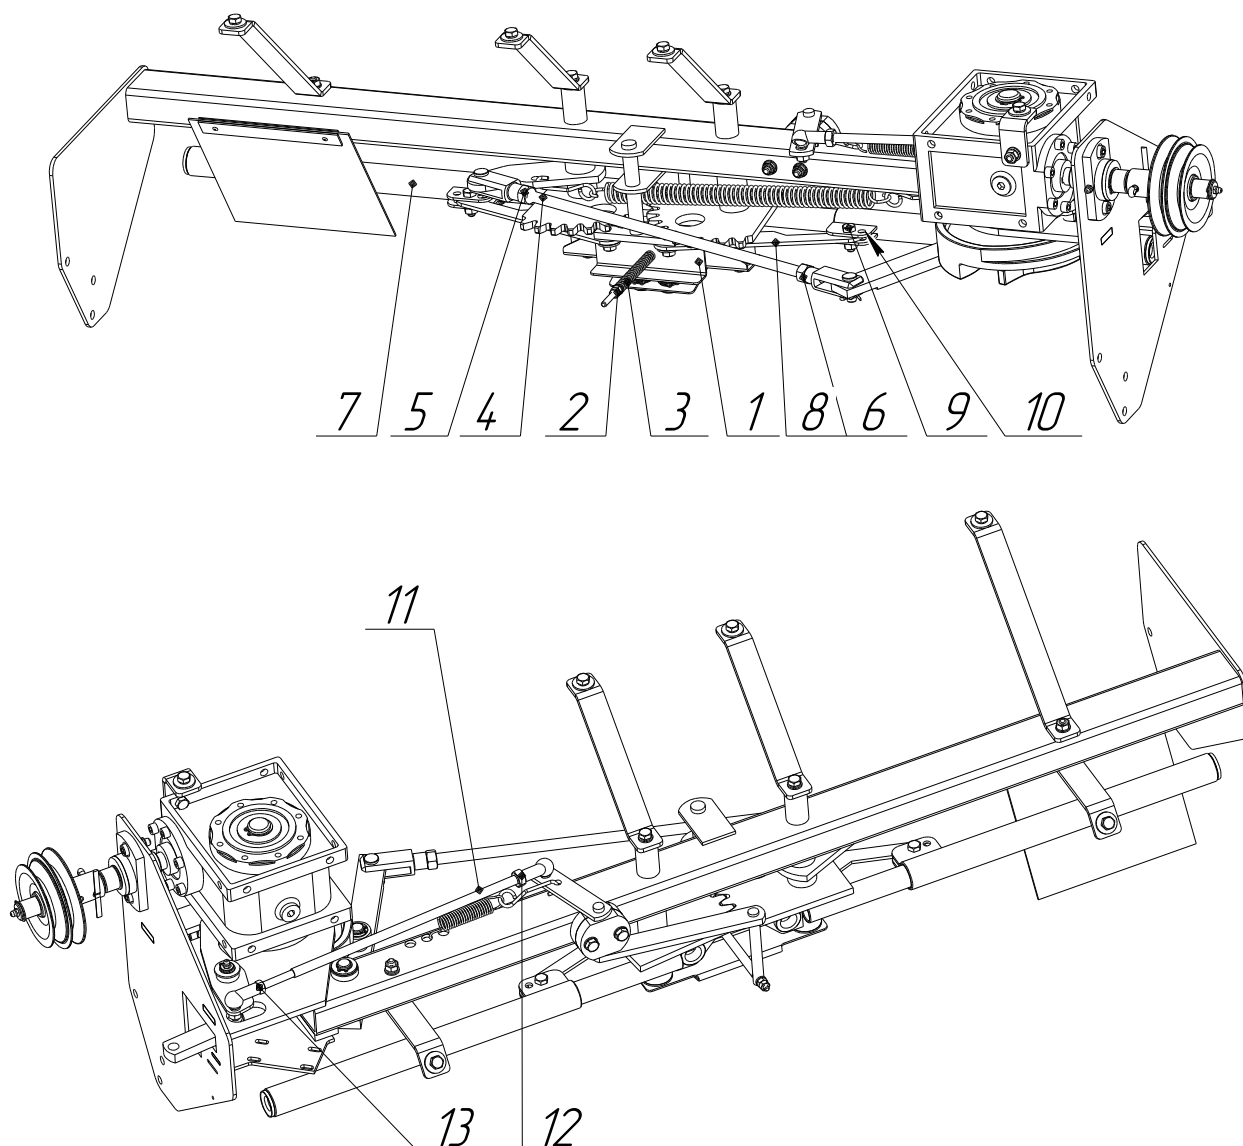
Регулировки механизма обвязки шпагатом: 1 – тормоз шпата; 2 – гайки М6; 3 – пружина тормоза шпата; 4 – тяга направляющих шпата; 5 и 6 – контргайки М12; 7 – направляющая шпата; 8 – рычаг направляющей шпата; 9
